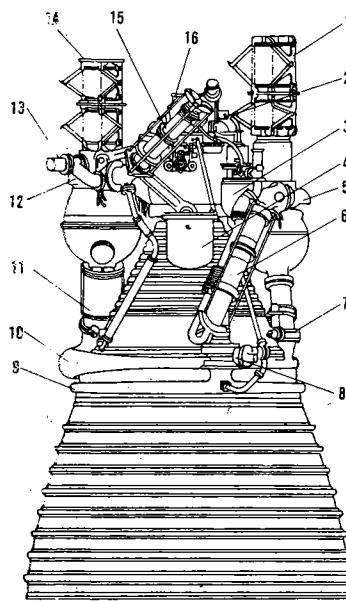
Motorul-rachetă american J-2: 1,6 — conducte pentru carburant; 2 — supapă pentru comburant; 3 — generator de gaze; 4 — echipament electric de comandă; 5 — pompă de carburant; 7 — supapă pentru reținerea comburantului; 8 — supapă principală pentru carburant; 9 — colector de carburant; 10 — colector de evacuare; 11 — schimbător de căldură; 12 — pompă de comburant; 13 — dispozitiv de dozare a compoziției propergolului; 14, 15 — conducte pentru comburant; 16 — sistem de suspensie cardanică.
